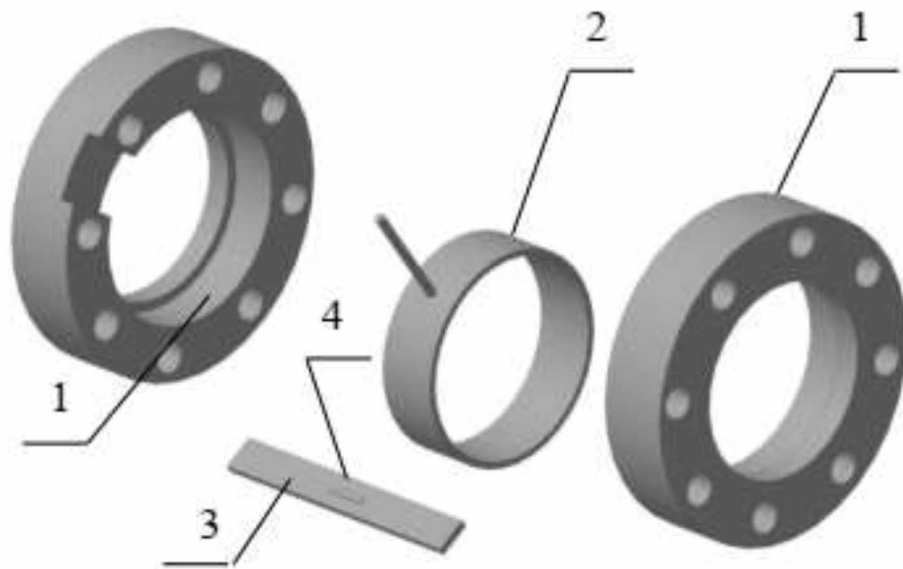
Пристрій для вимірювання крутних моментів: 1 - фланець; 2 - циліндрична вставка з важелем; 3 - пластина; 4 - тензодатчик
